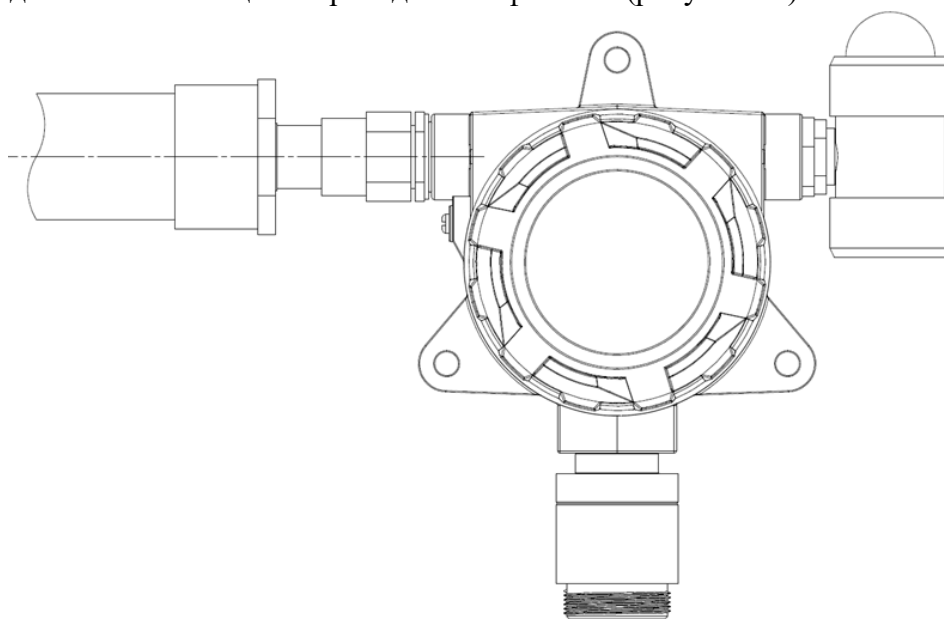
внешний вид газоанализатора, установленного на трубе
